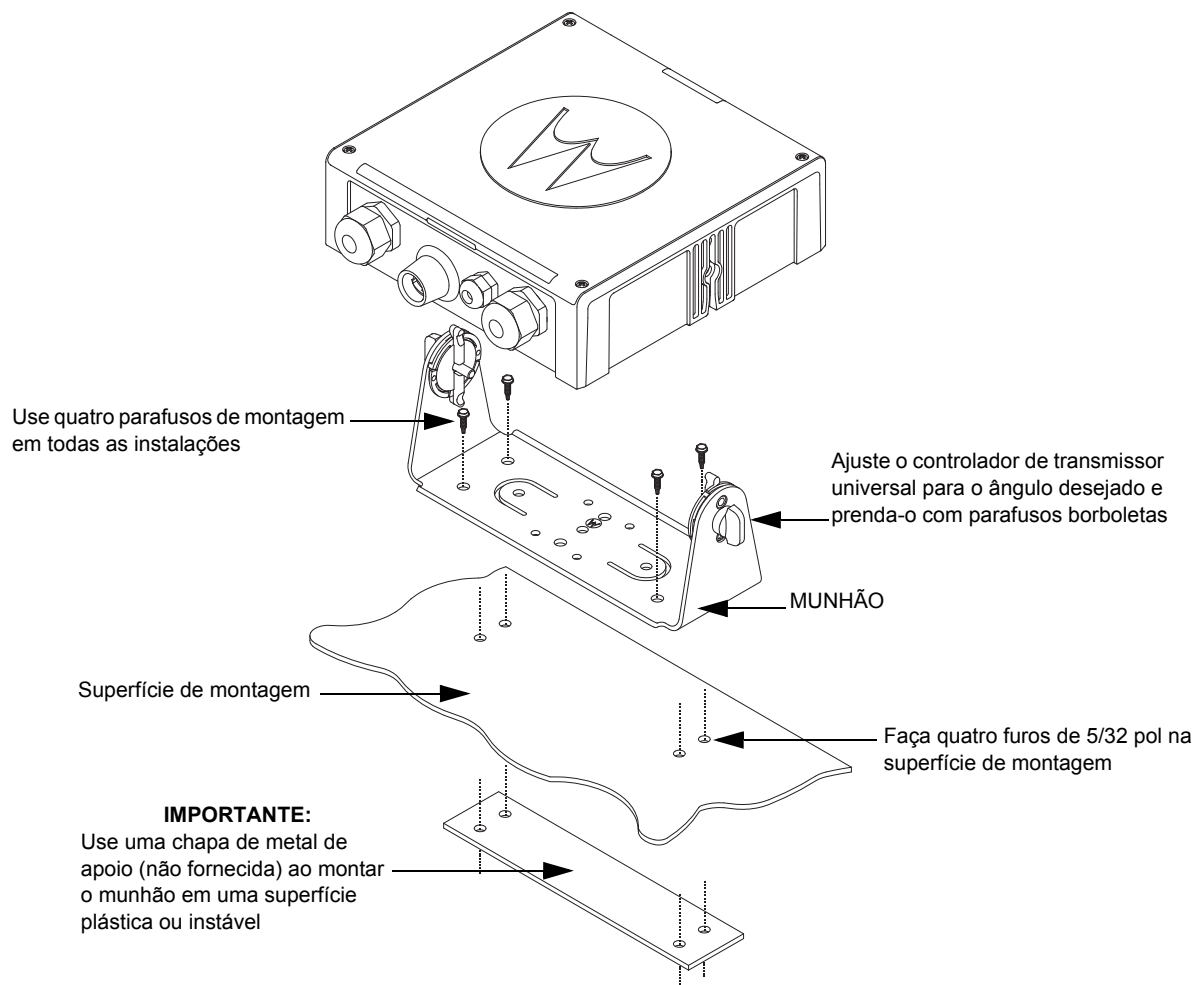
Vista Detalhada da Instalação do Controlador de Transmissor Universal
